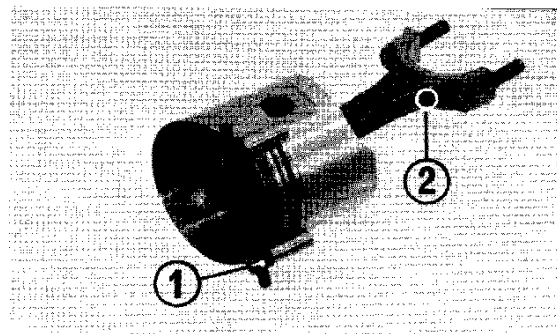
(1) Kolbenring-Einführwerkzeug
